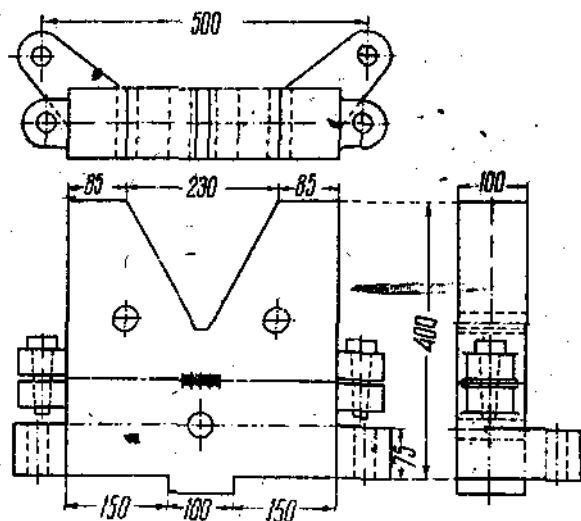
V-образные колодки для термитной сварки коленчатого вала.
